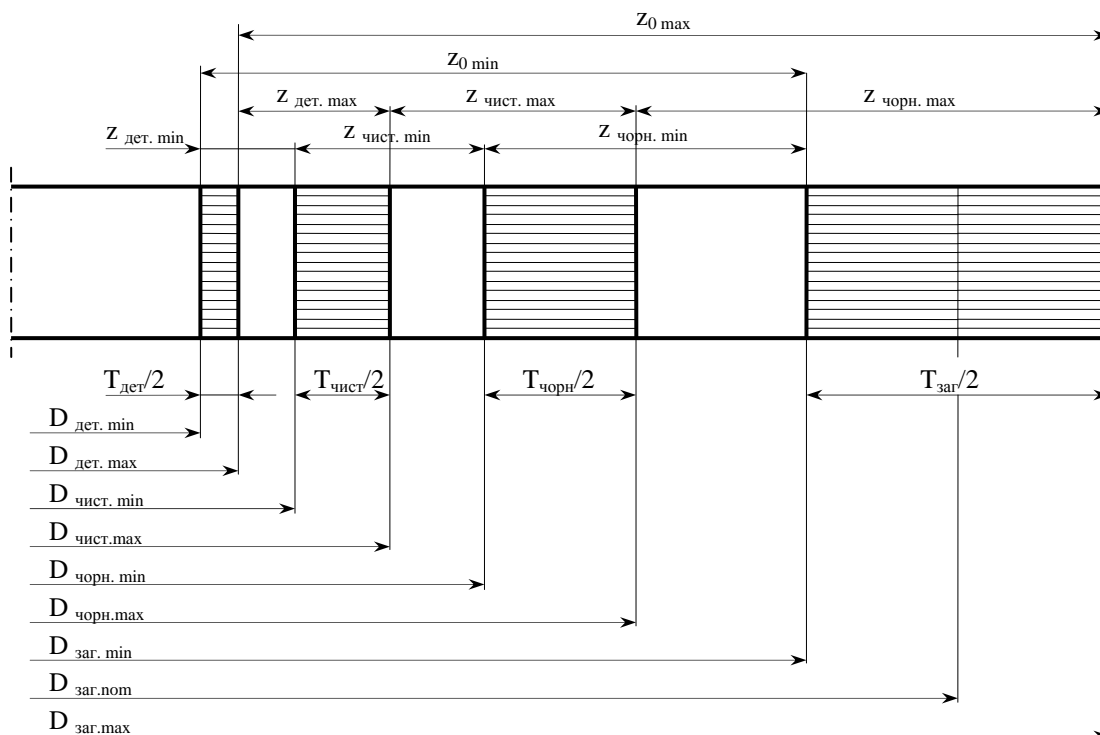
Схема розміщення припусків і допусків на оброблення валу на попередньо налагоджених верстатах
